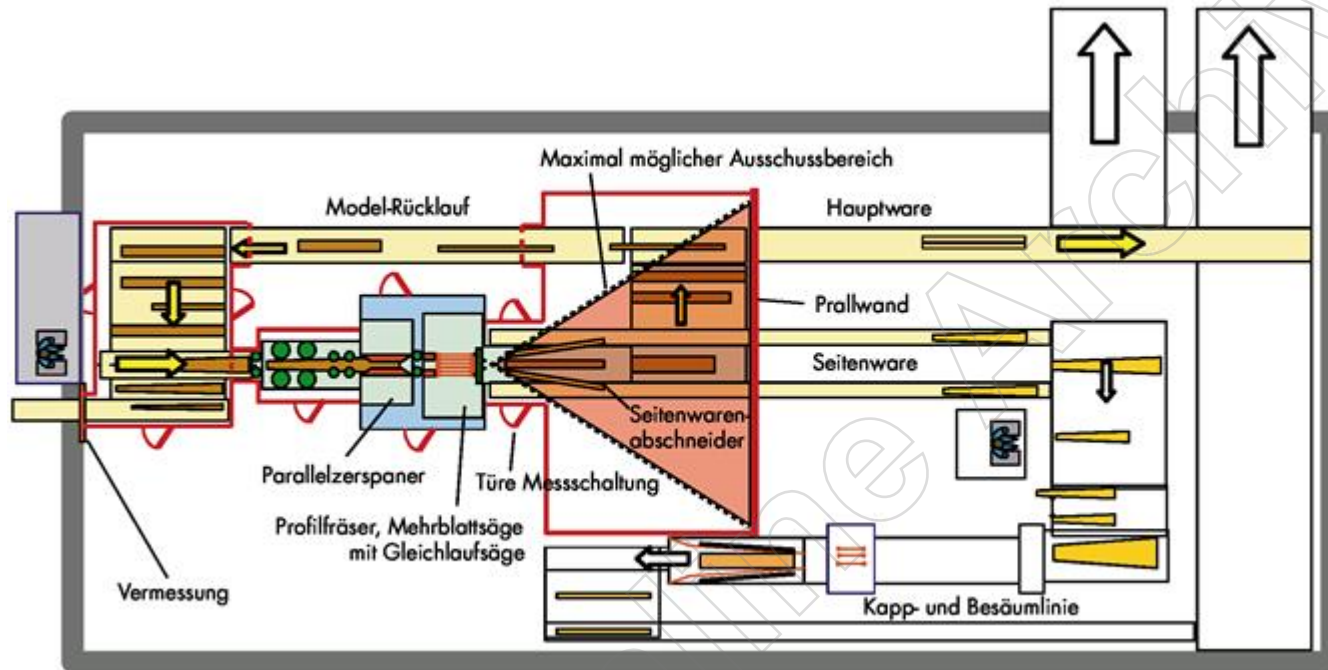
Layout "Universal-Spanerlinie": Ausschussbereich eingeengt durch fangende Schutzrichtungen (tunnelartiger Blechkanal)
